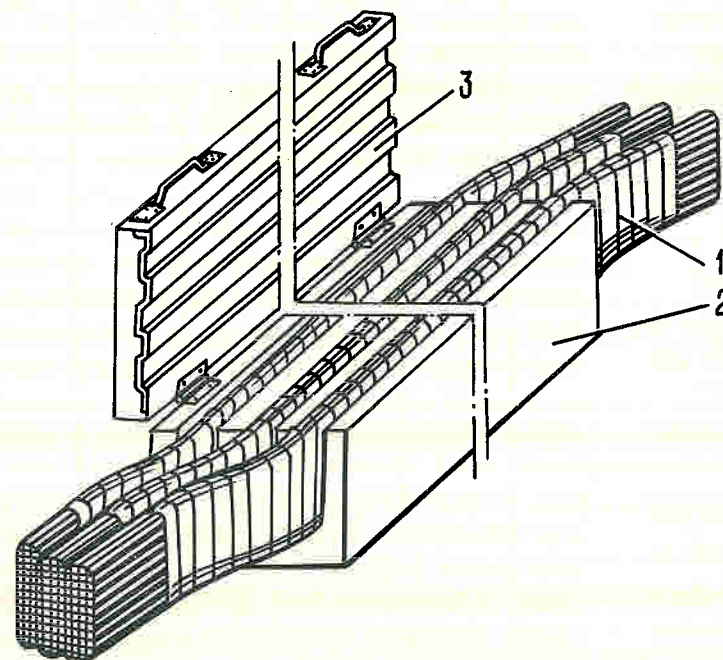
Приспособление для испытания электрической прочности изоляции верхних стержней обмотки статора перед укладкой в пазы: 1 — стержни статора; 2 — деревянная коробка с пазами, облицованными медной фольгой; 3 — крышка
